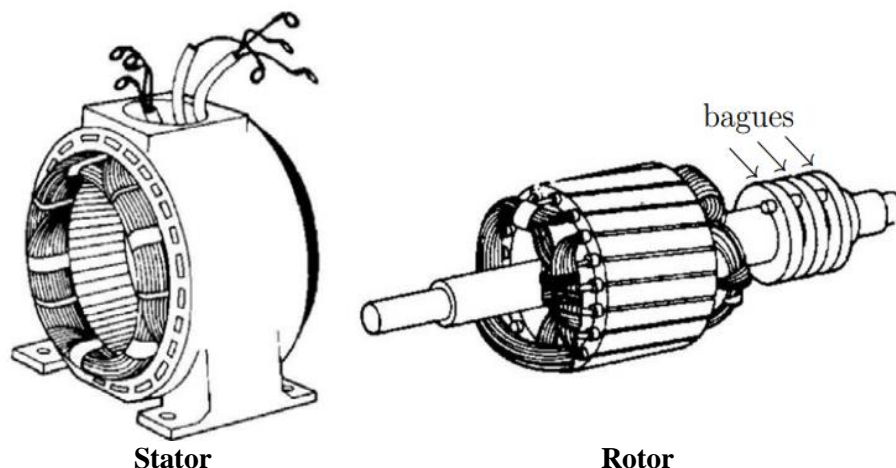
Stator et rotor de la machine asynchrone à rotor bobiné [Bonnet, 2008]
